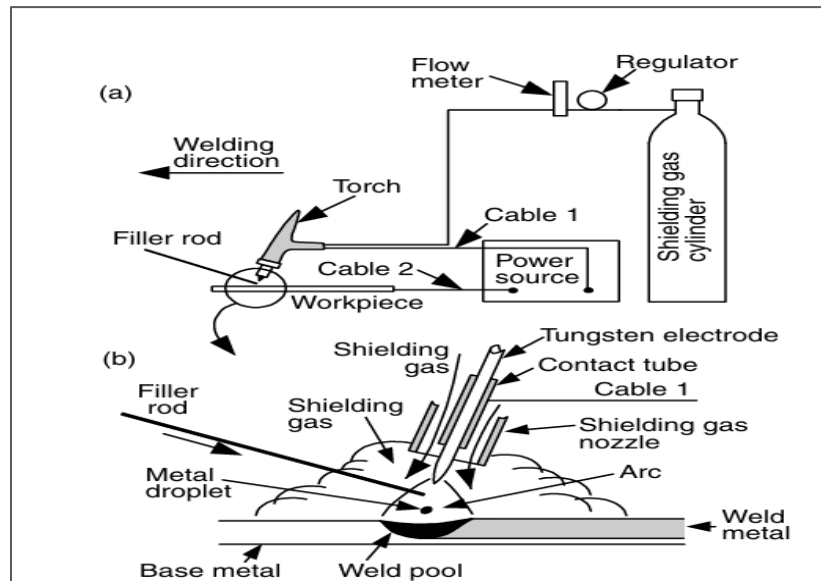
Soudage à l'arc gaz-tungstène : (a) processus global ; (b) zone de soudage agrandie.
